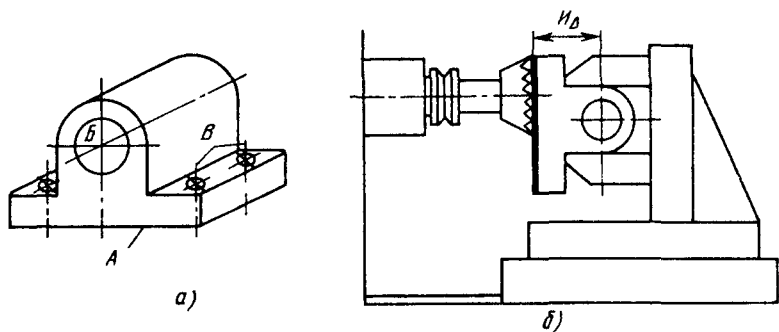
Корпус (а) подшипника и схема (б) получения размера на многоцелевом станке с отсчетом перемещений от оси литого отверстия благодаря использованию контактной головки:
